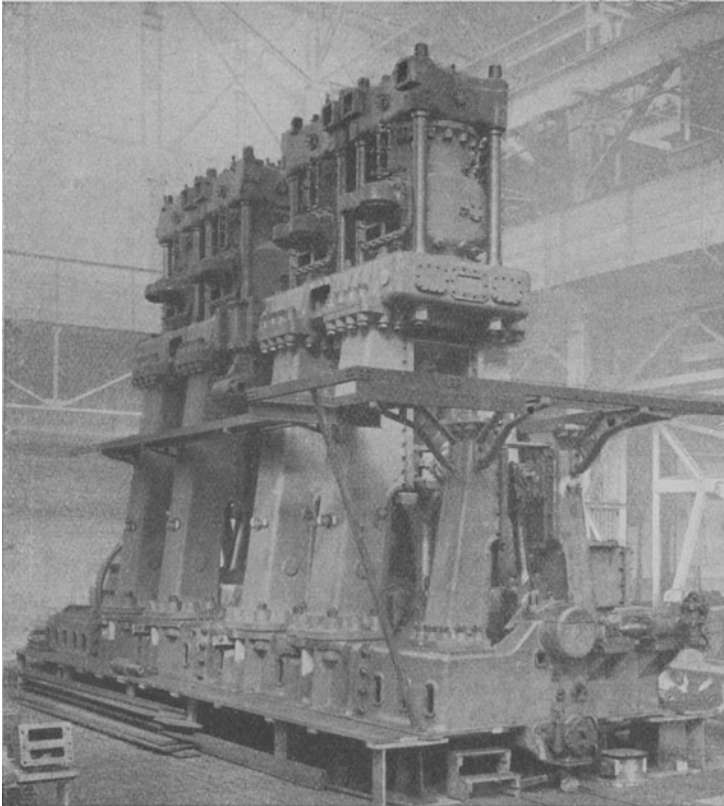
Vierzylinder-Zweitakt-Ölmaschine.
